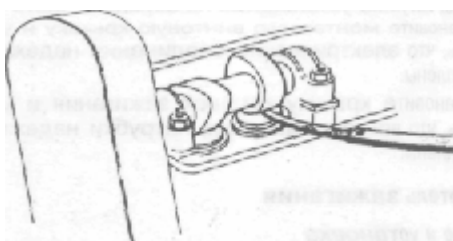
Проверка зазоров клапанов, цилиндр N 1 двигателя B230F и B230FT
